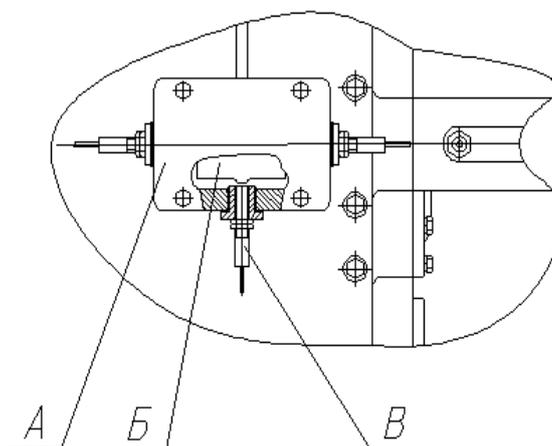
Схема аварийной установки нейтрали коробки передач
